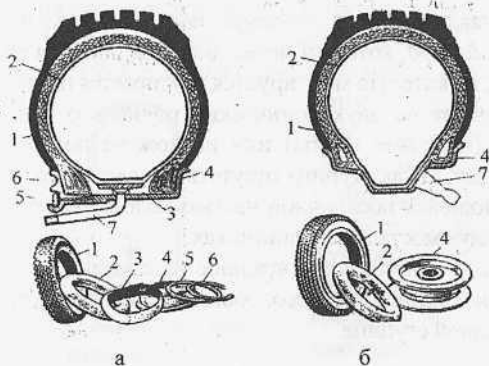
Камерные шины: а – для плоского обода; б – для глубокого обода; 1 – покрывка; 2 – камера; 3 – ободная лента; 4 – диск колеса; 5 – бортовое кольцо; 6 – замочное кольцо; 7 – вентиль
